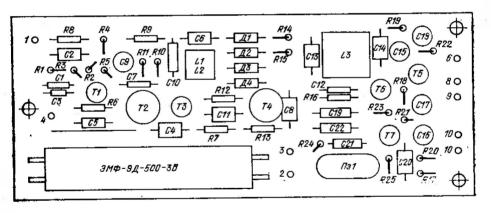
Монтажная схема платы усилителя ПЧ (вид сверху)
